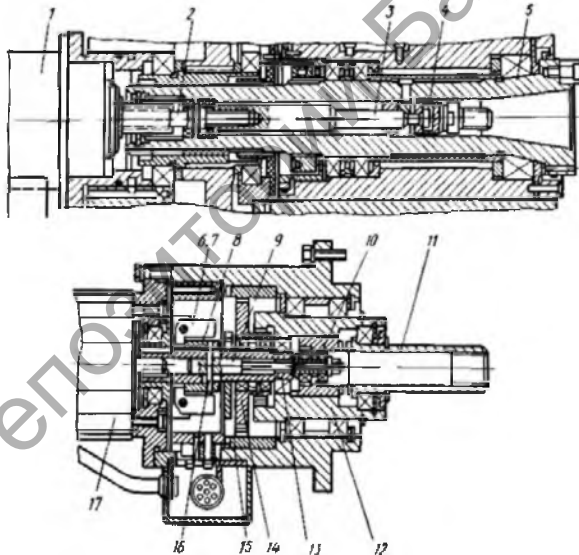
Устройство электромеханического зажима инструмента станка мод. 6Р13Ф3-37
